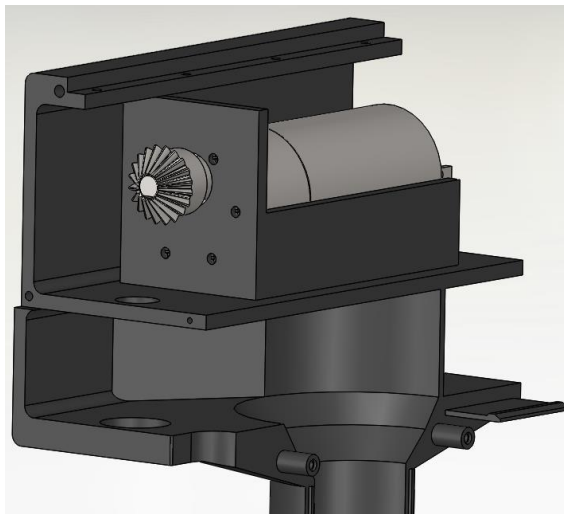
Colocación de Engranaje Cónico de Inglete en el Eje del Motor.
